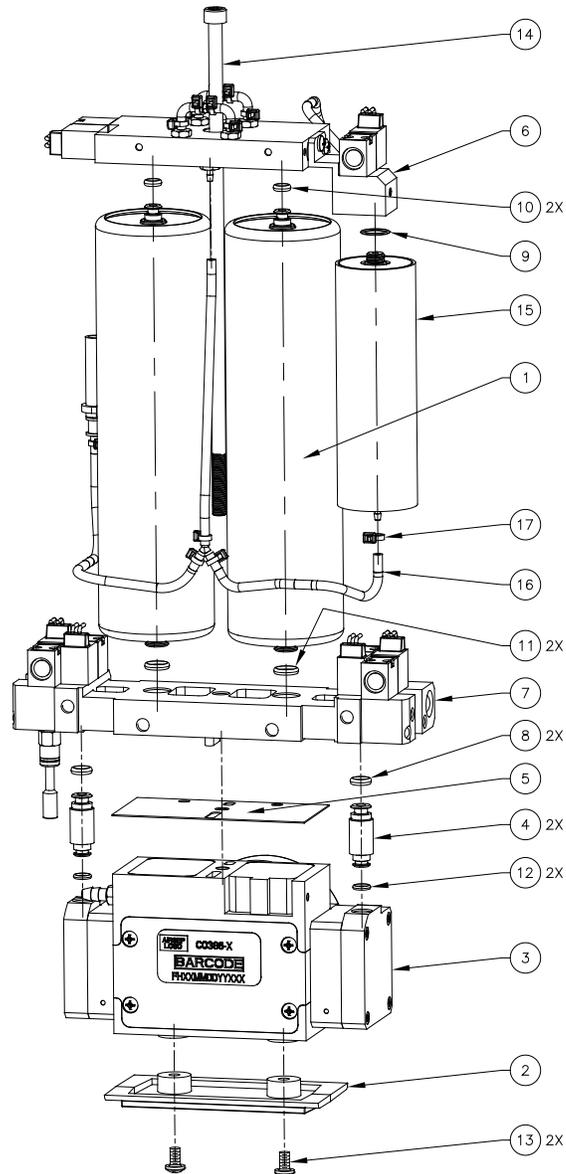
PRV-Baugruppe - Explosionsansicht
